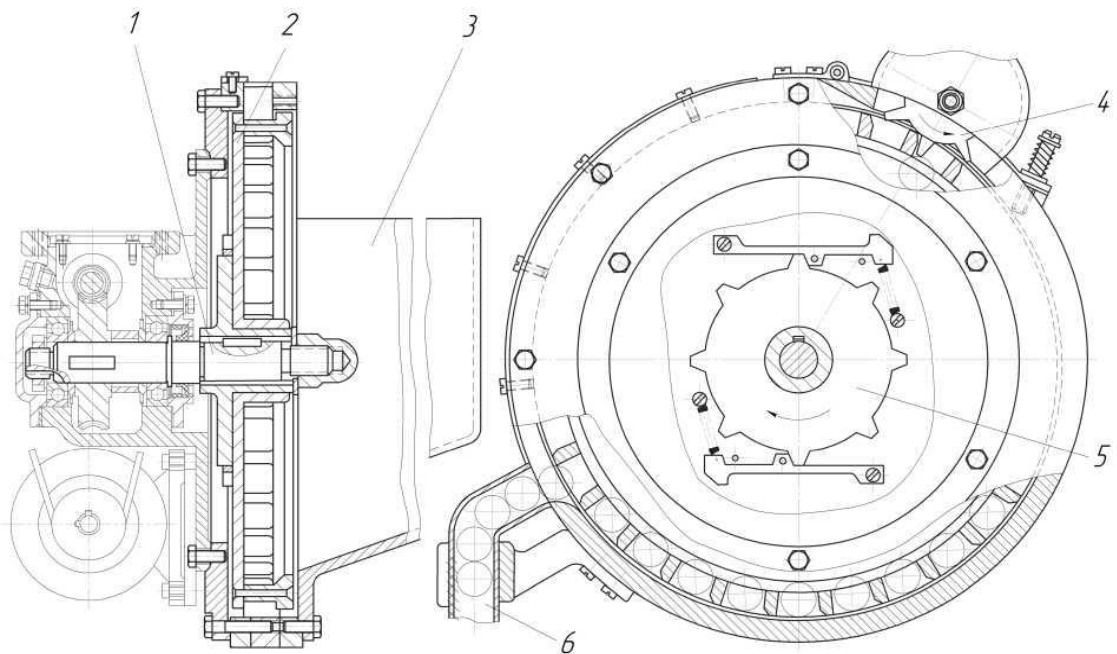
Механічний дисковий вертикальний комірковий бункерний завантажувальний пристрій для металевих і пластмасових ковпачків, що закручуються: 1 – вал; 2 – диск; 3 – бункер; 4 – зірочка для виштовхування неправильно орієнтованих та застряглих ковпачків; 6 – приймач
